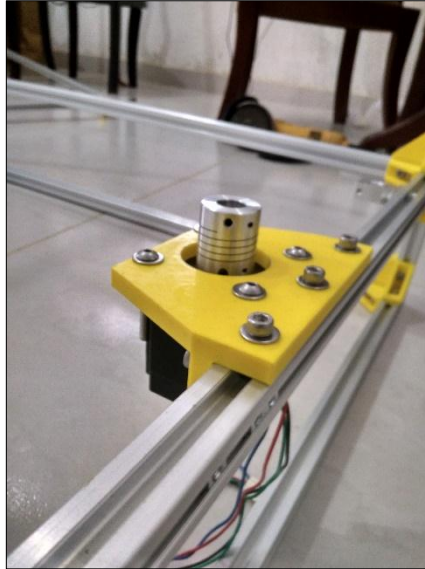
Soporte del motor eje "Z". Fuente: Autor, 2017
